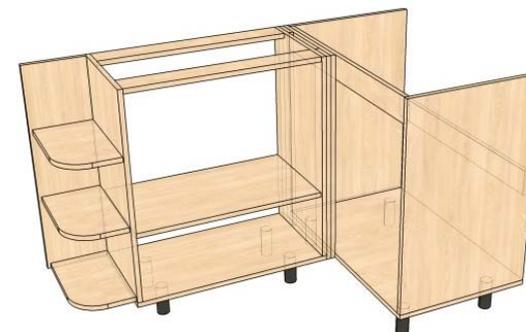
Схема соединения углового короба к глухой стенке мойки
